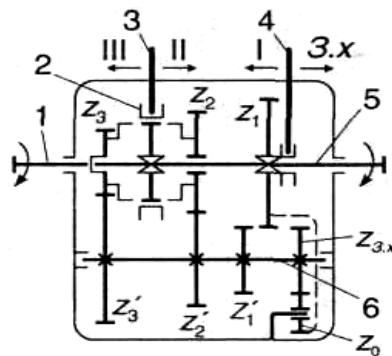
Схема триступінчастої коробки передач: 1 – ведучий вал; 2 – синхронізатор; 3, 4 – вилки; 5 – ведений вал; 6 – проміжний вал
